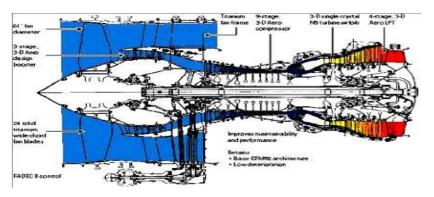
Vue en coupe du moteur CFM56-7B [11].
